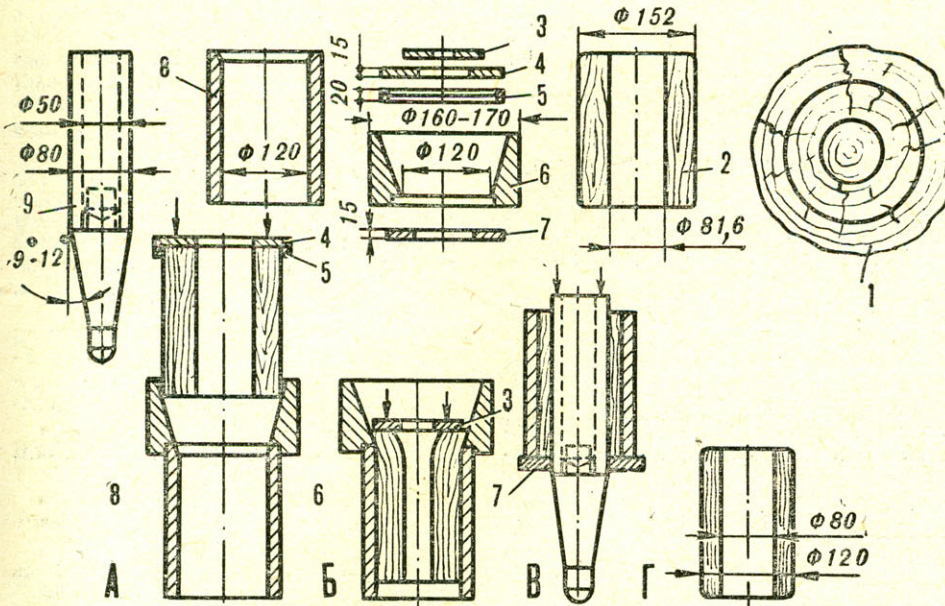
Контурное прессование: 1 — разметка черновой заготовки; 2 — цилиндр-заготовка; 3, 4, 7 — шайбы; 5 — кольцо; 6 — приемный корпус; 8 — готовая пресс-форма; А — пресс-форма с заготовкой под прессом; Б — запрессованная заготовка; В — запрессовка пуансона; Г — заготовка после прессования и сушки. Все размеры даны ориентировочно.
